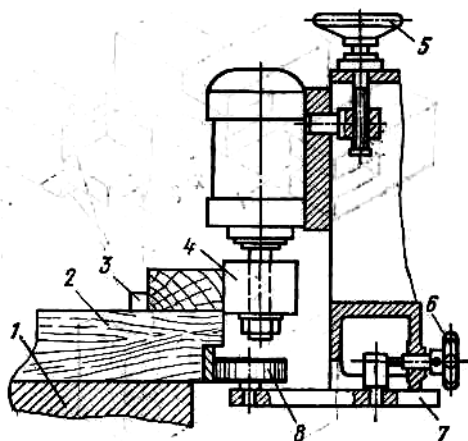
Настройка опорного ролика карусельного фрезерного станка: 1 — карусельный стол, 2 — копир, 3 — упор, 4 — фреза, 5 — маховичок настройки фрезерного суппорта по высоте, 6 — маховичок настройки опорного ролика, 7 — ползун, 8 — опорный ролик;
